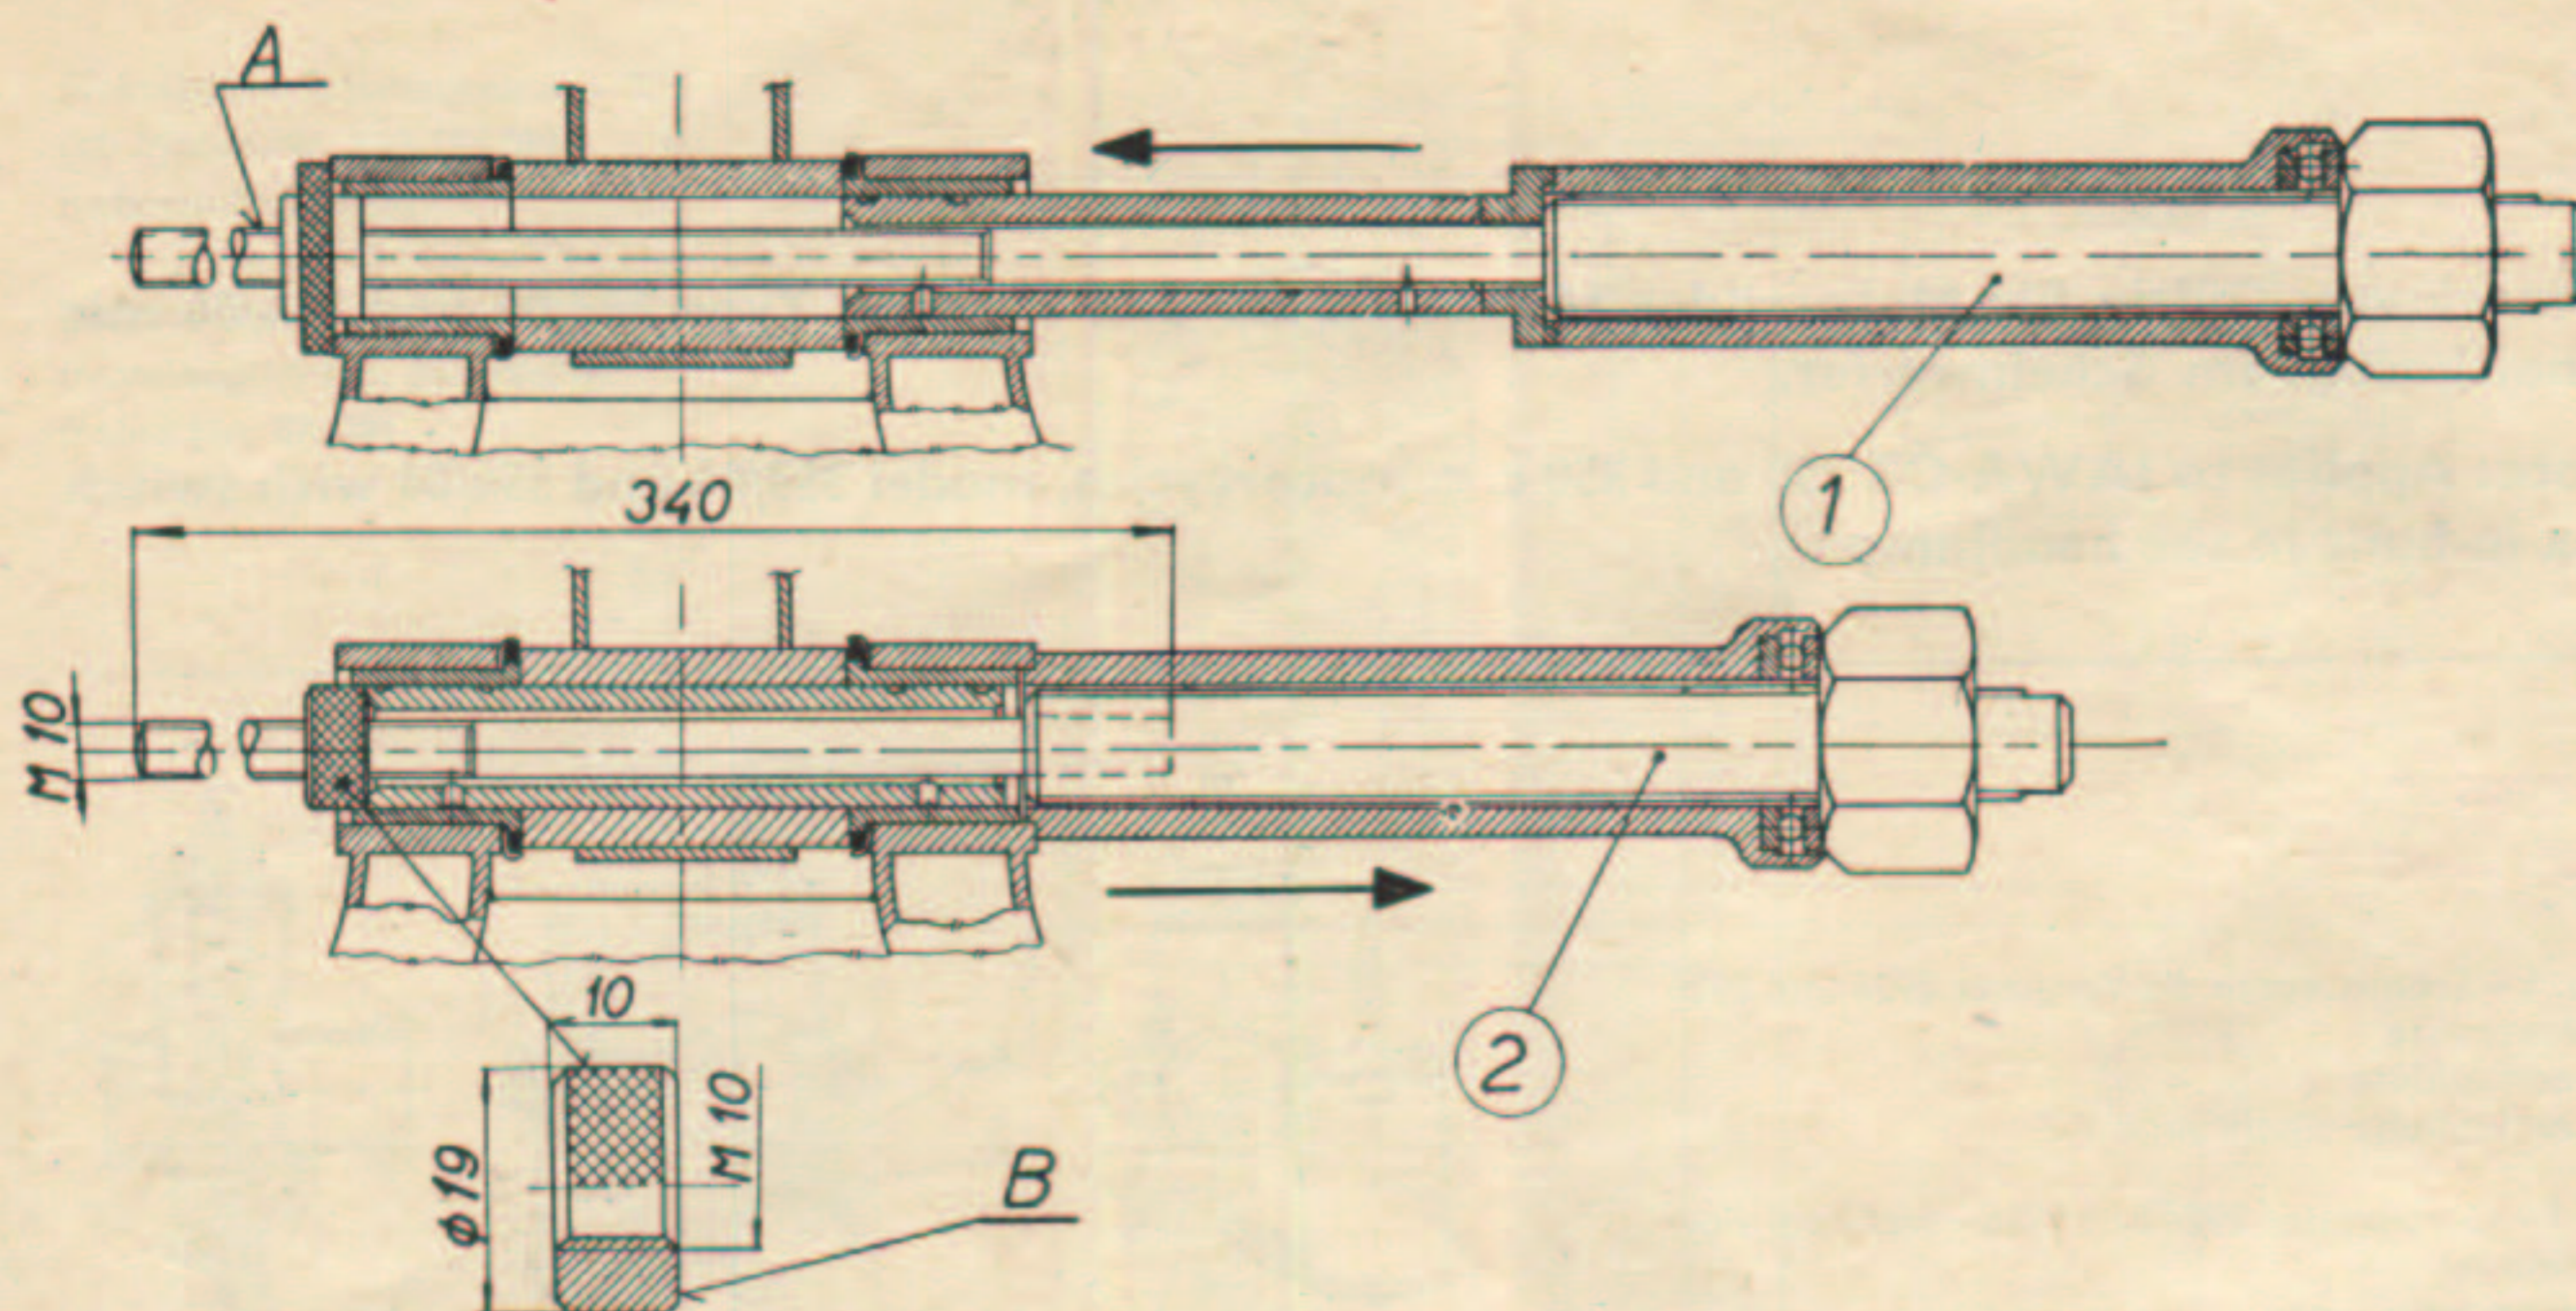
Anwendung des Abziehers für den Schwinggabelbolzen
